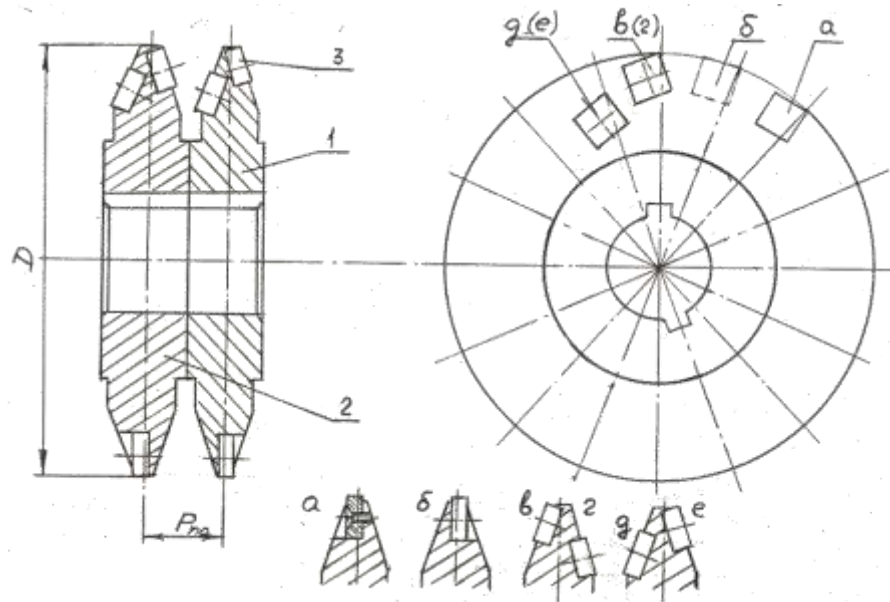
Дискова фреза з механічним кріпленням багатогранних твердосплавних пластин
